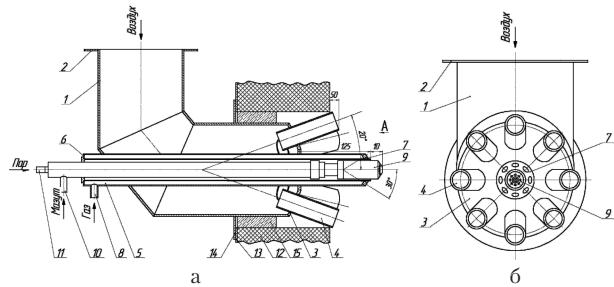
Конструкция многофакельной горелки: а — общий вид; б — вид А.
